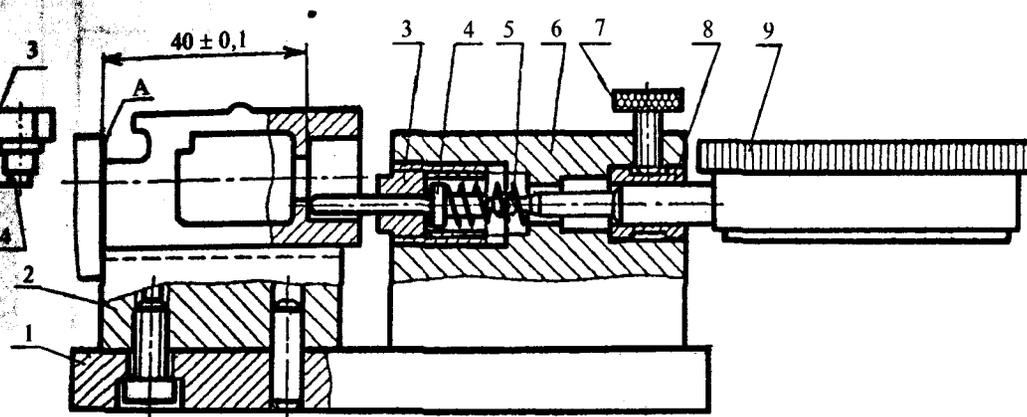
Приспособление для контроля внутреннего линейного размера:
